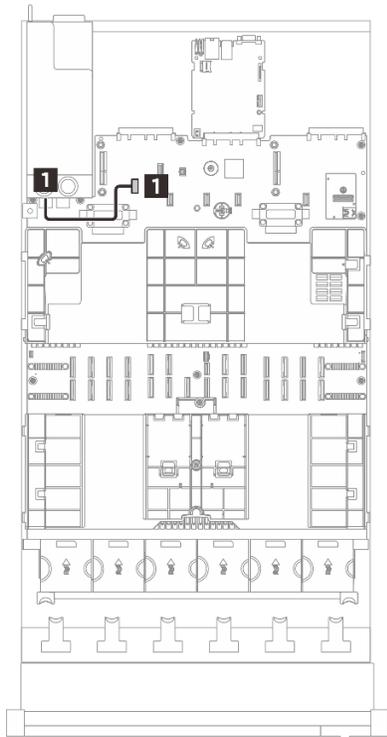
Disposición de los cables para la placa de la distribución de alimentación
